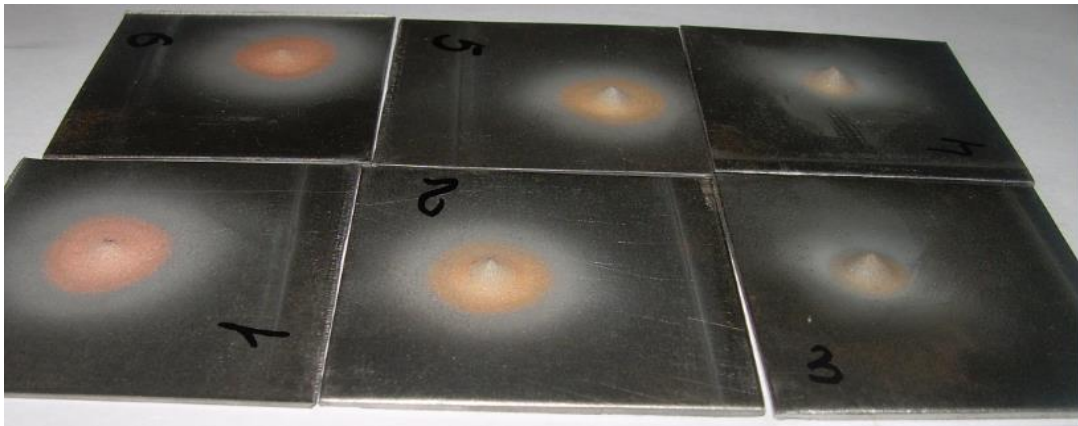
Сталеві пластини з напиленими плямами покриття
